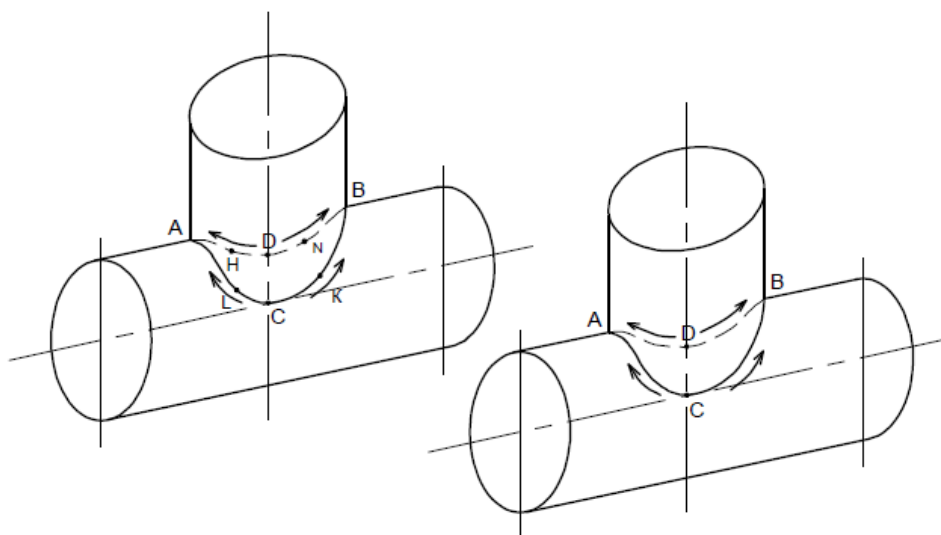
Последовательность заварки углового сварного соединения трубопровода (сварка штуцера)
